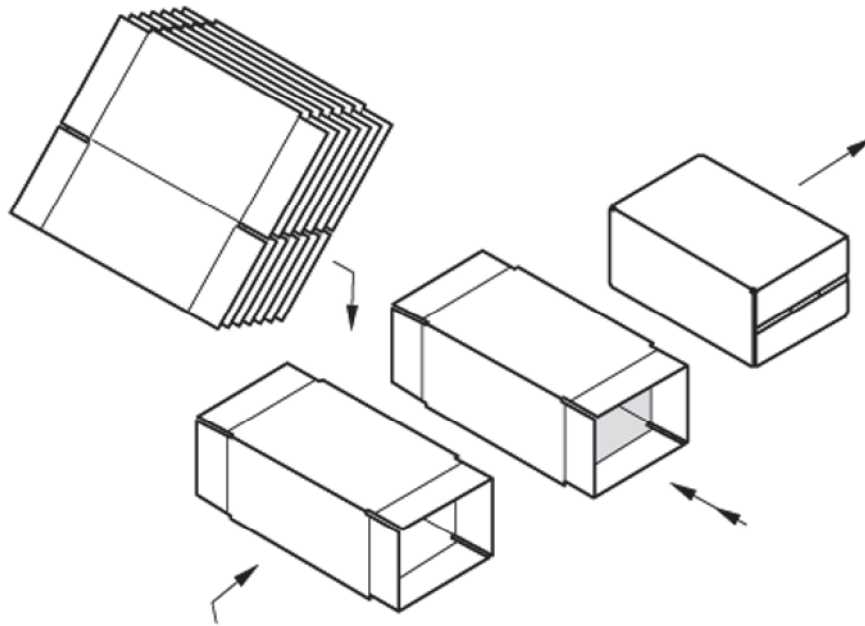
Horizontal-Faltschachtelverpackungsmaschine
